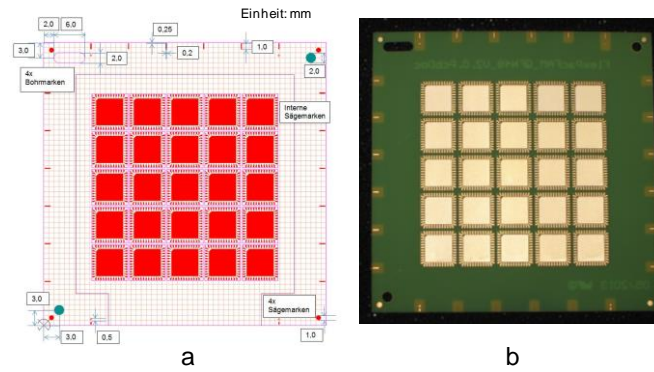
a) Zeigt das Top-Layout des QFN48 7x7 LN-Design mit 25 Montageflächen und b) zeigt die Top-Lage des gefertigten QFN48 7x7 LN.
